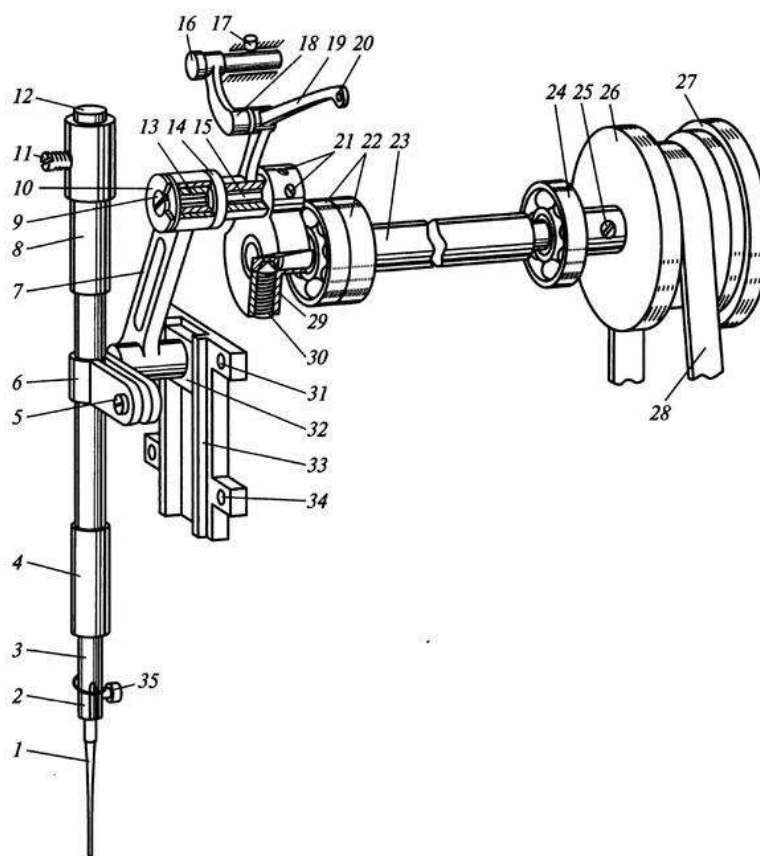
Механизм иглы и нитепротягивателя машины 1022-М кл.
